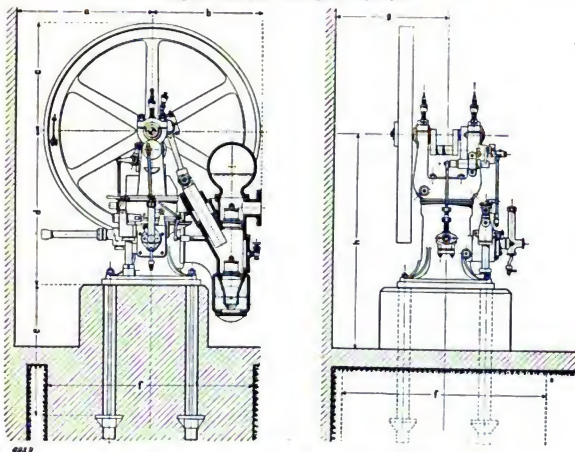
und 278. Motorpumpe der Gasmotorenfabrik „Deutz“.
